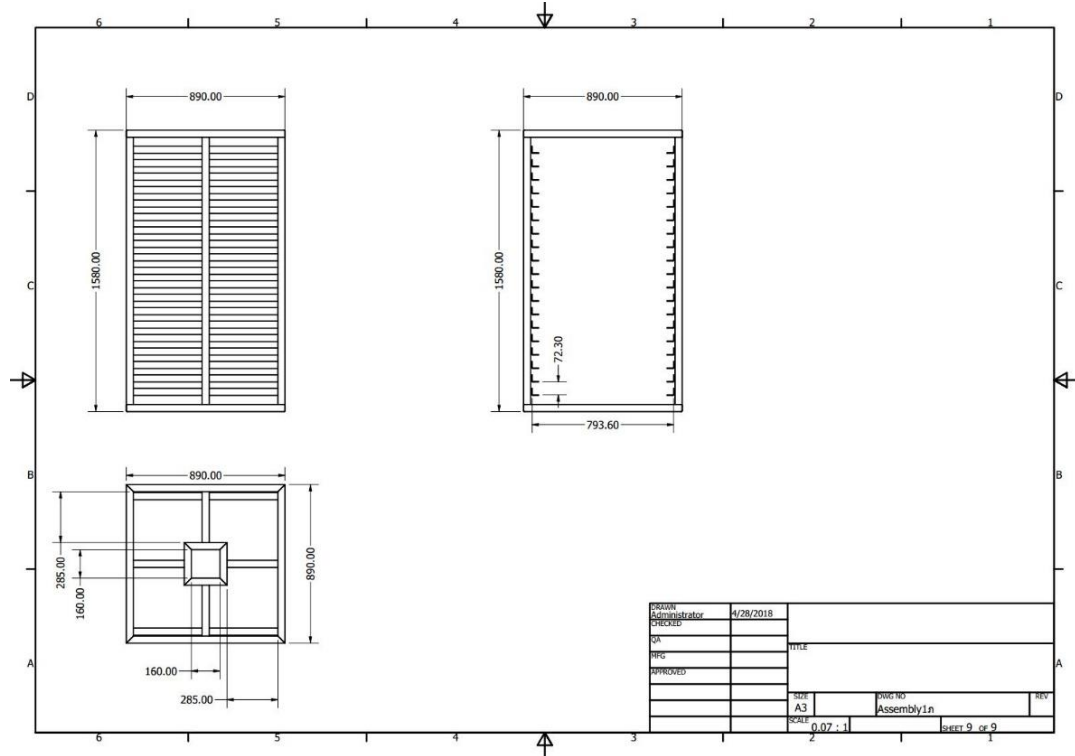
แบบ (Drawing) เครื่องหั่นกล้วย
